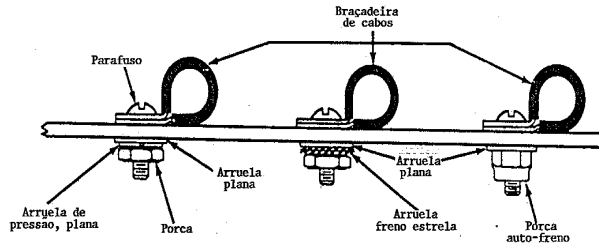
Ferragens típicas de montagem para braçadeiras de cabo.
